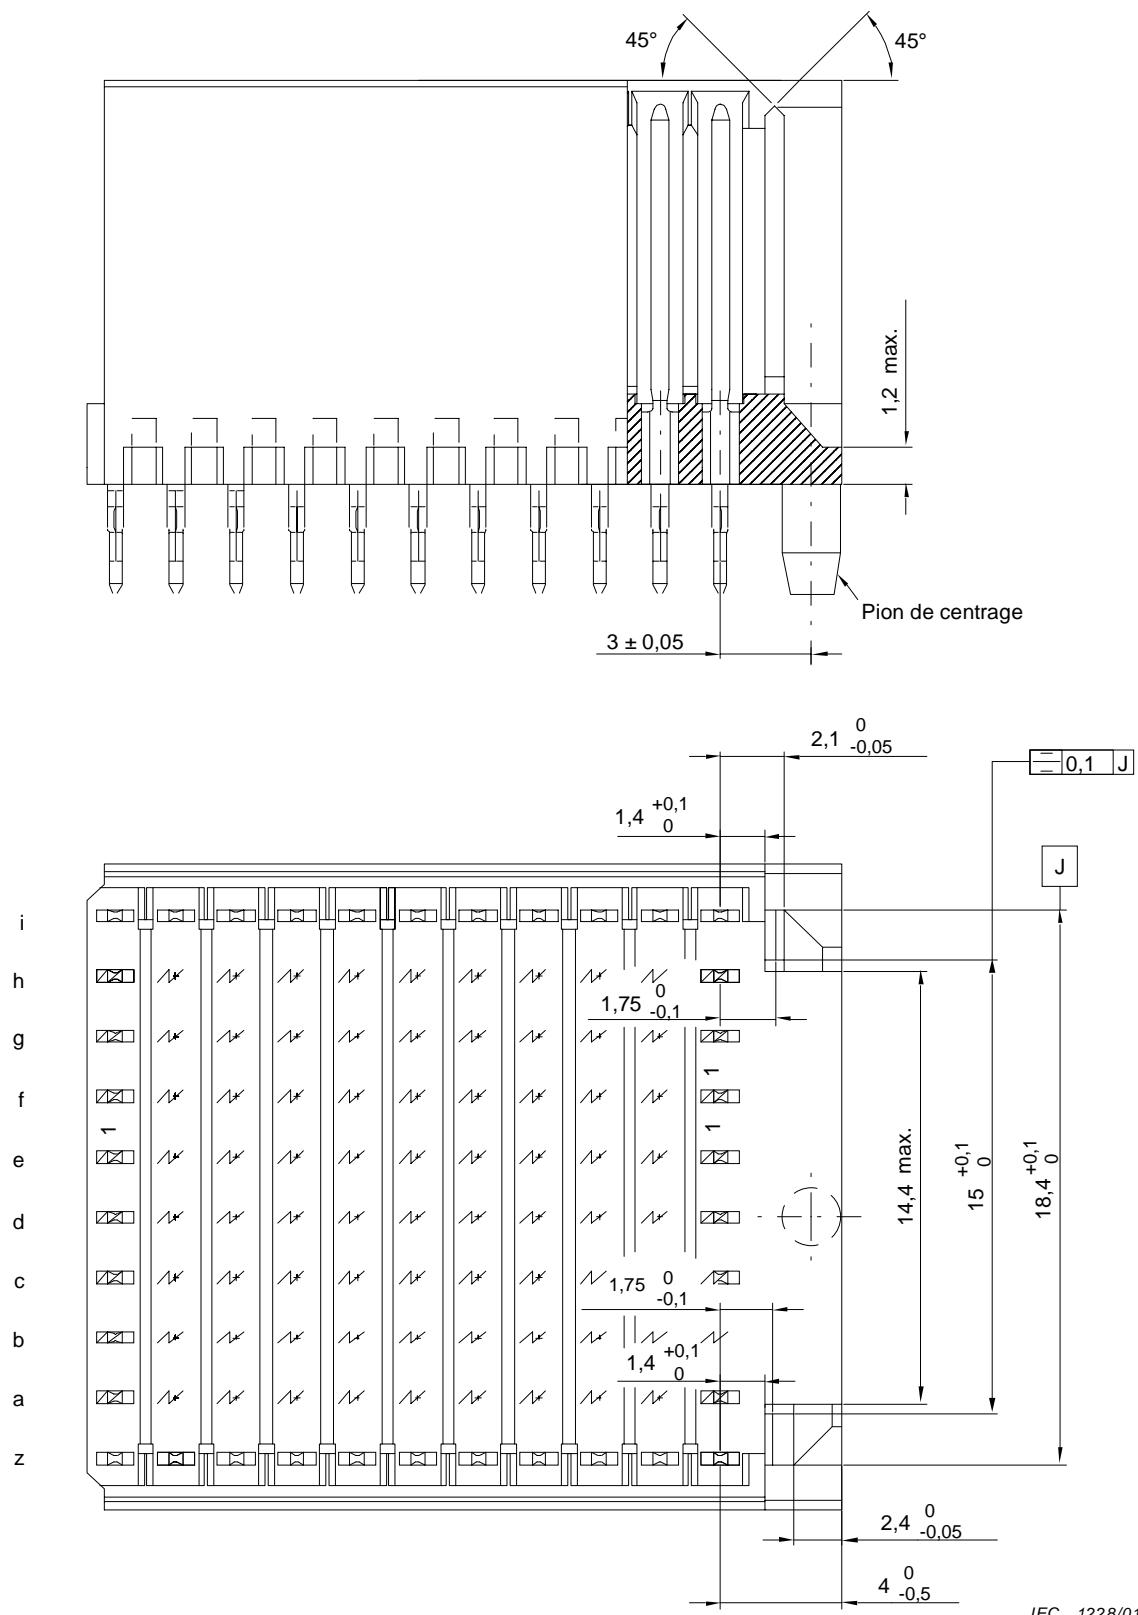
Dimensions du modèle F, module d'extension d'embase 25 mm
